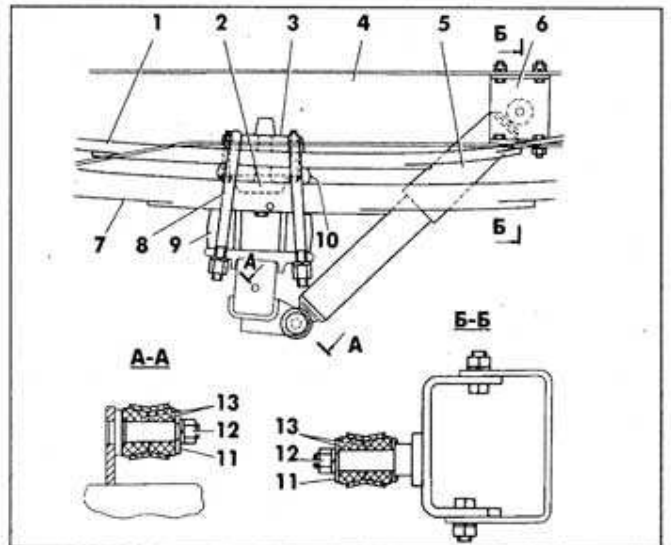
Задняя подвеска автомобилей типа 4x4: 1 – дополнительная рессора; 2 – буфер с прокладкой; 3 – наклад-ка; 4 – лонжерон рамы; 5 – амортизатор; 6 – кронштейн амортизатора; 7 – основная рессора; 8 – стремянка; 9 – подкладка рессоры; 10 – прокладка; 11 – шайба; 12 – гайка; 13 – резиновая втулка.
